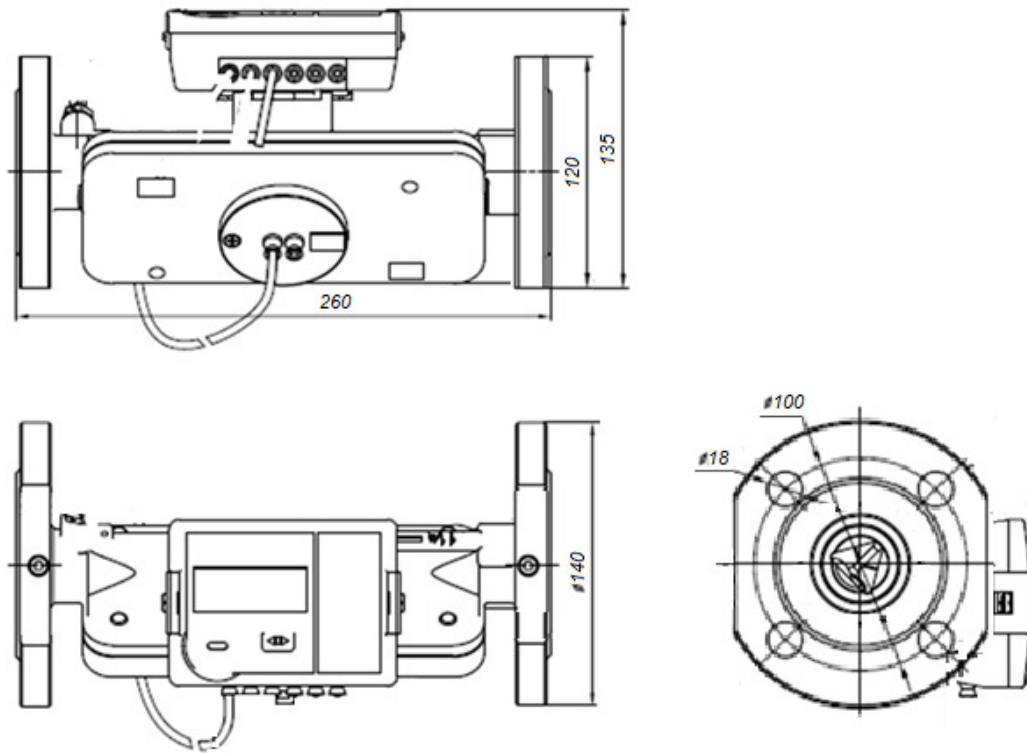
Присоединительный размер к трубопроводу Ду32, длина L=260 мм.
